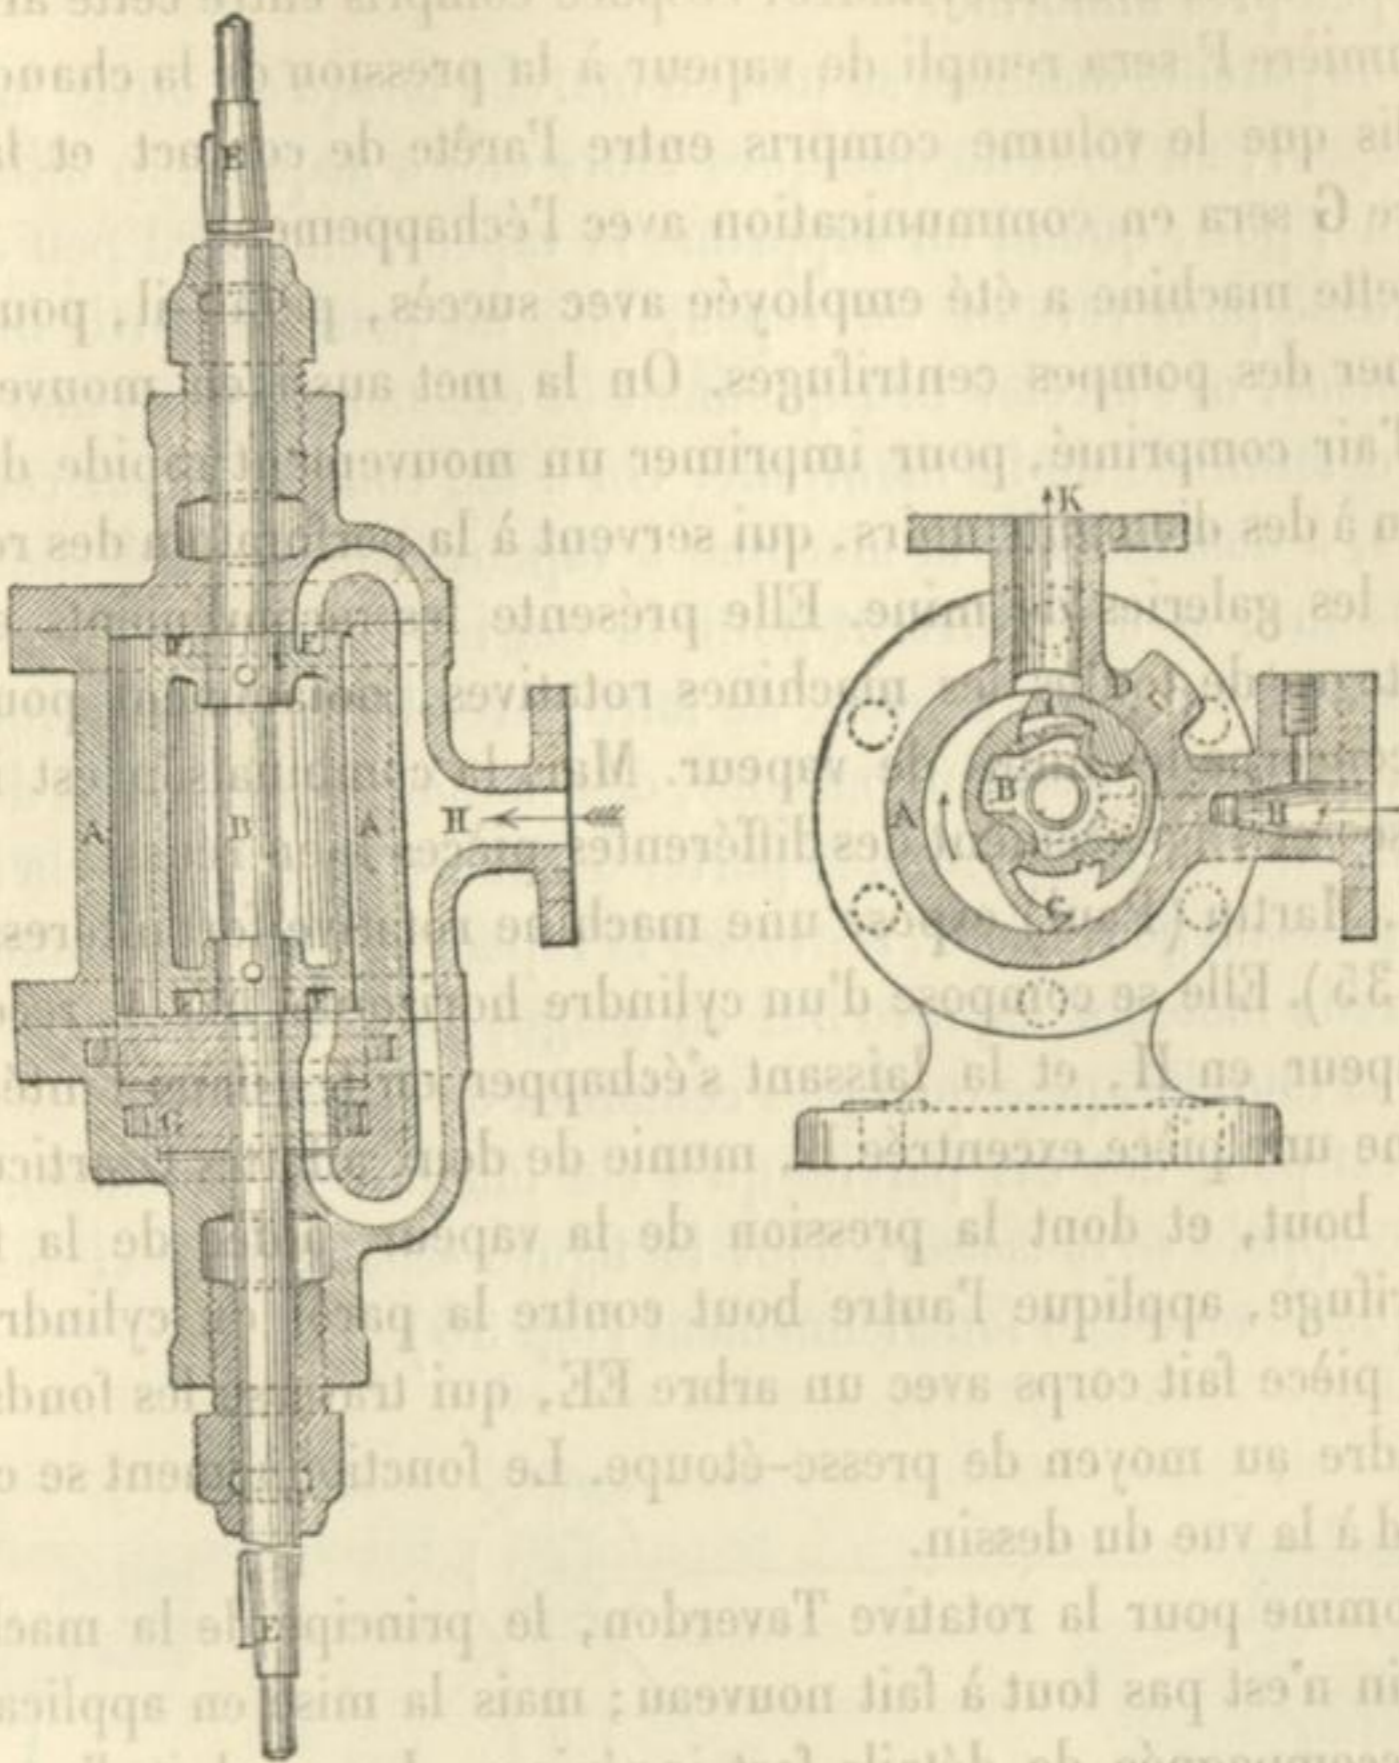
Machine à vapeur rotative de Paul Martin.
